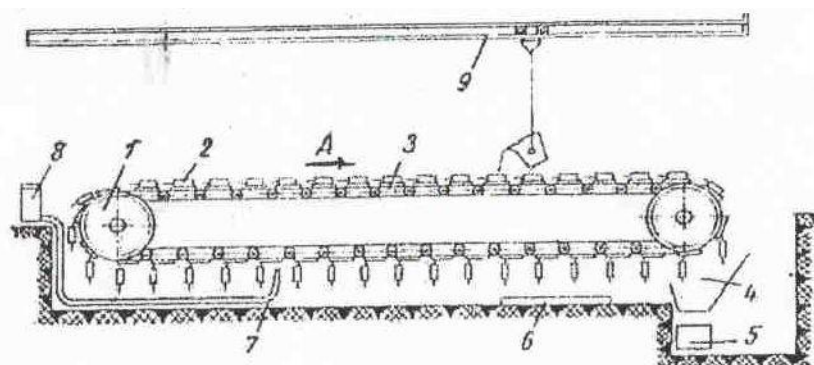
Вертикально-замкнутый кокильный конвейер: 1 — колесо; 2,3 — цепь; 4 — лоток; 5 — ящик; 6 — сопло; 7 — пульверизатор; 8 — бак; 9 — передача.
